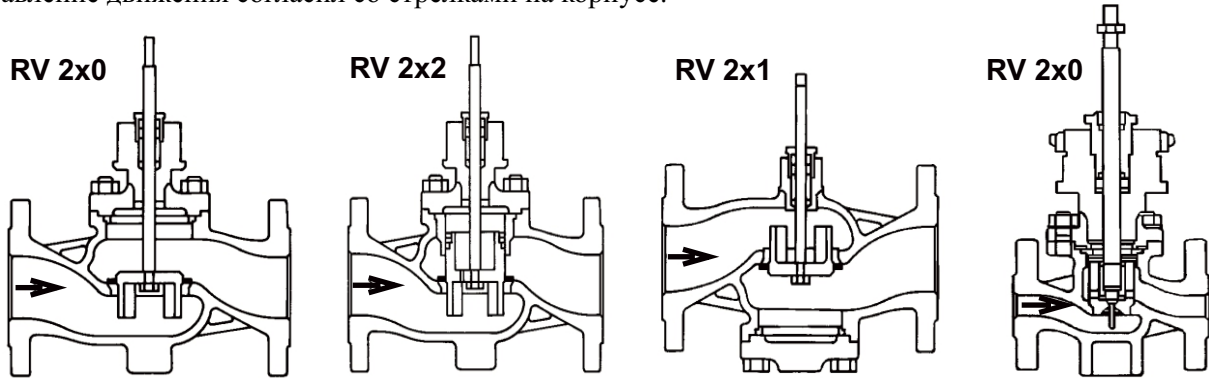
Направление потока через двухпутевую арматуру с цилиндрическим или форматированным конусом RV 2xx xxx xxxx Lx xx/xxx-xxx (Харак. L; R; P; S; U)
